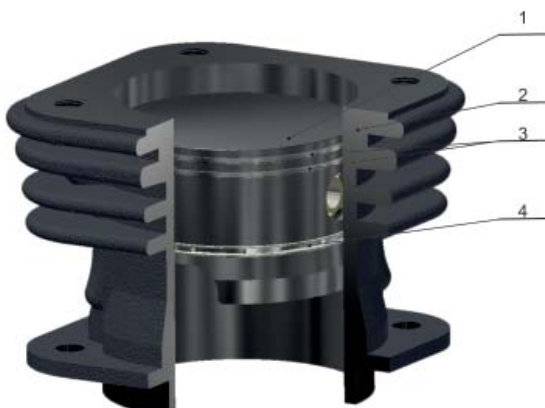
ЦПГ компрессора в сборе: 1 – поршень; 2 – цилиндр; 3 – кольца компрессионные; 4 – кольцо маслоъемное
